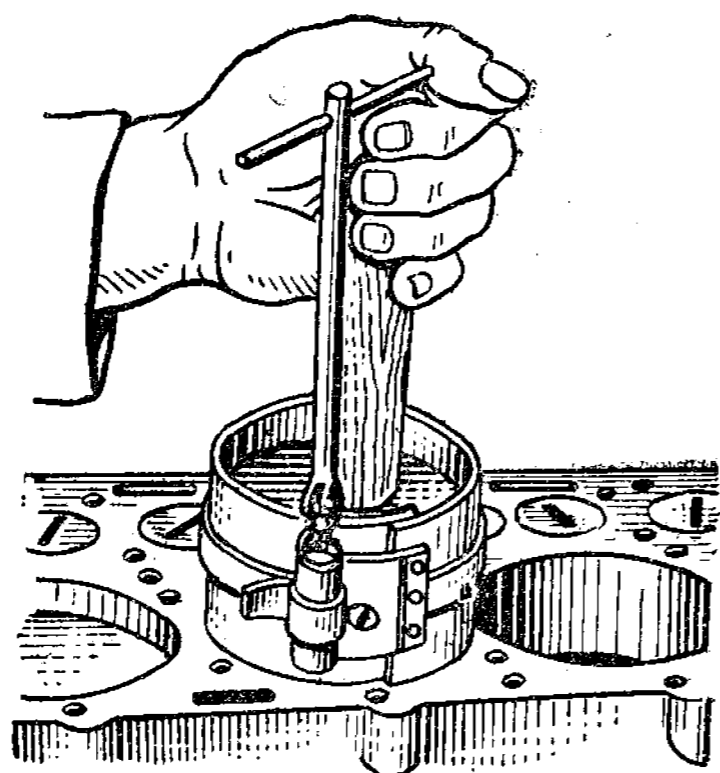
Установка поршня в сборе с кольцами в цилиндр
